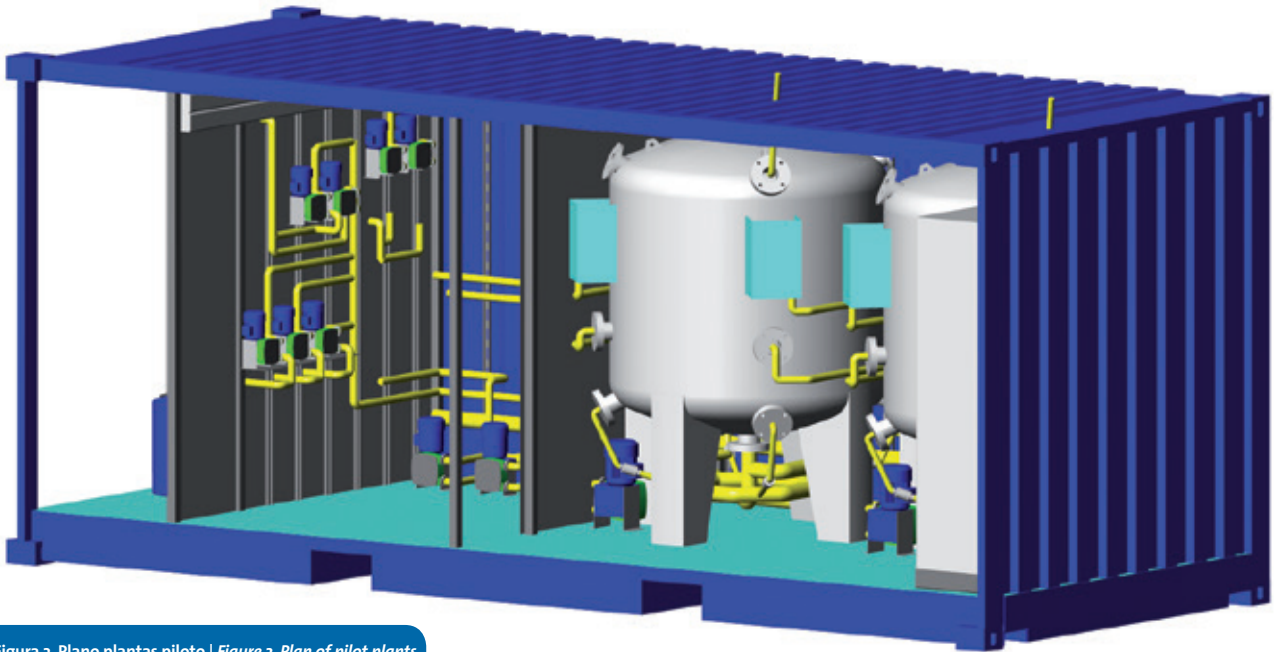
Plano plantas piloto | Figure 3. Plan of pilot plants
